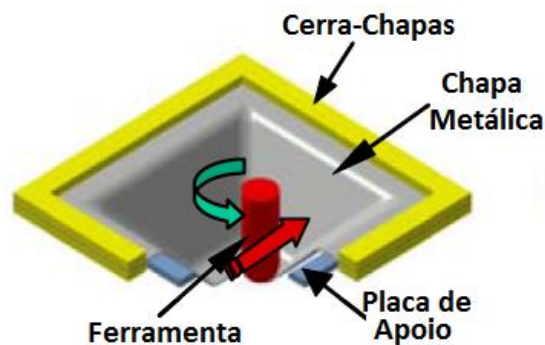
| Estampagem Incremental de Único Ponto [9].
